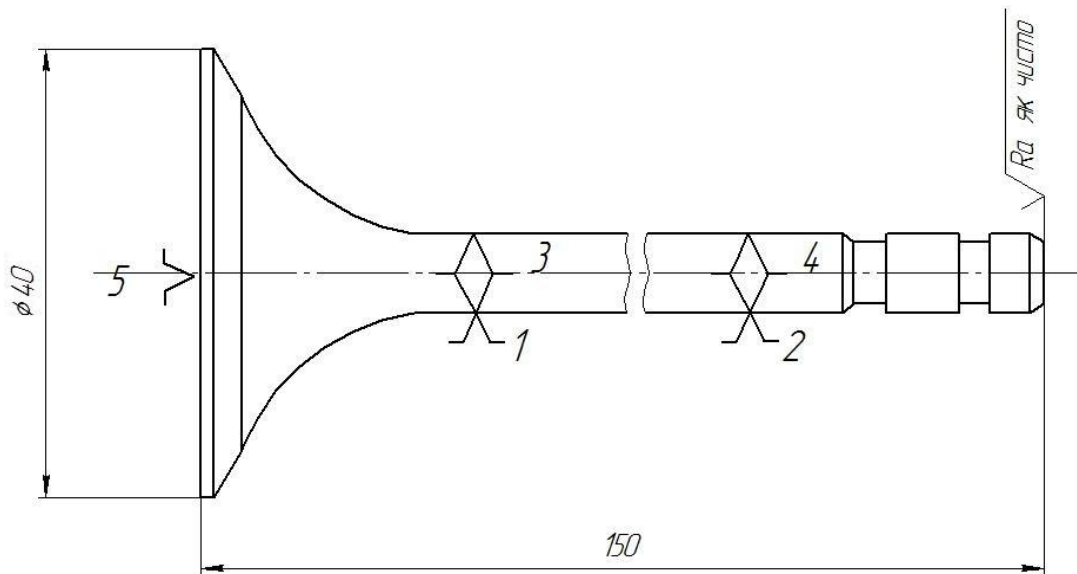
Ескіз впускного клапана метод базування при обробці шліфувальній
